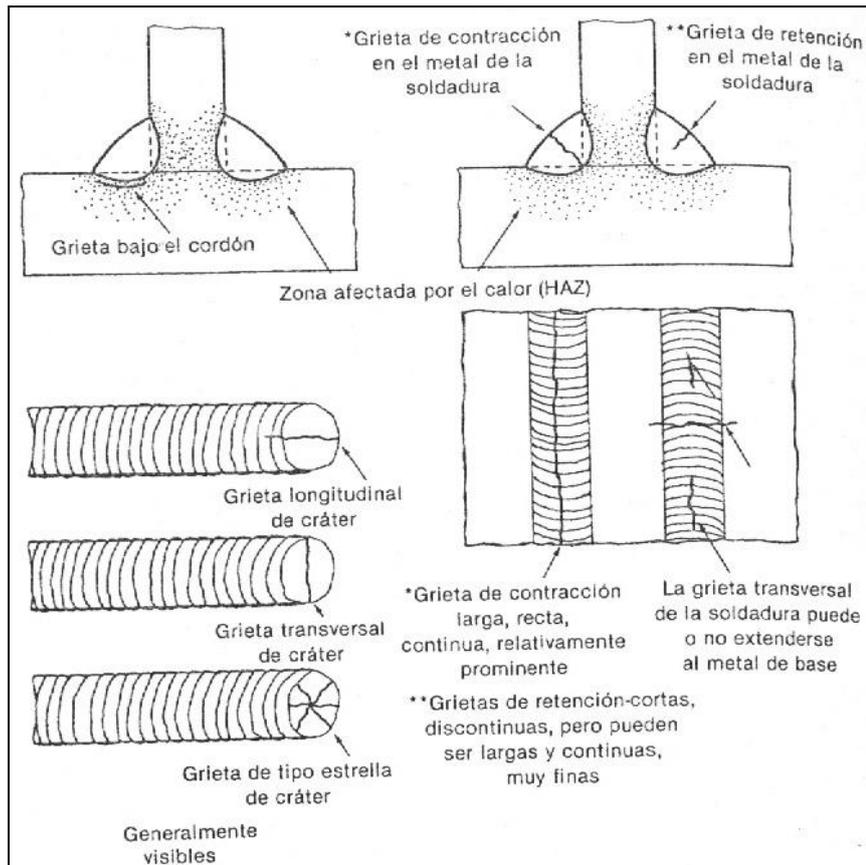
Tres clases básicas de grietas de soldadura
